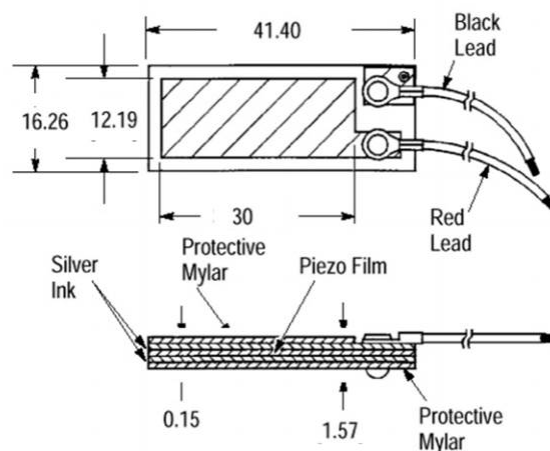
Dimensions (en mm) du LDT28K de Measurement-Specialties
